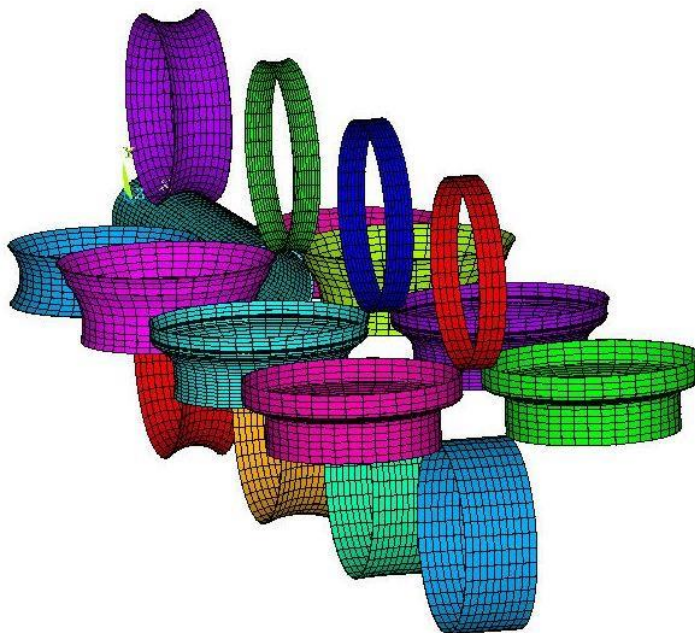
Разбиение поверхностей валков и заготовки на КЭ перед началом расчета процесса формообразование гнутого профиля замкнутого сечения
